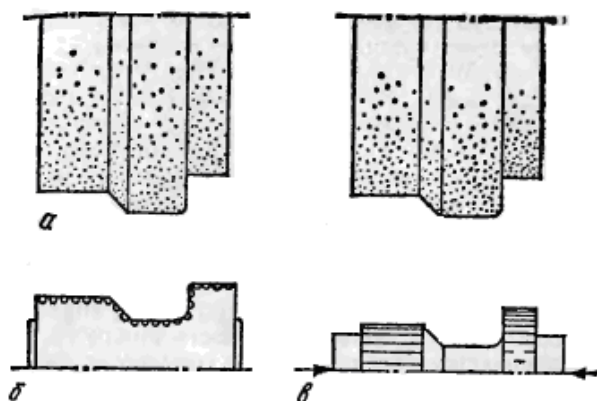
Схема правлення при паралельному положенні осей круга та ролика: а – шліфувальний круг; б – правлячий ролик; в – оброблена деталь
